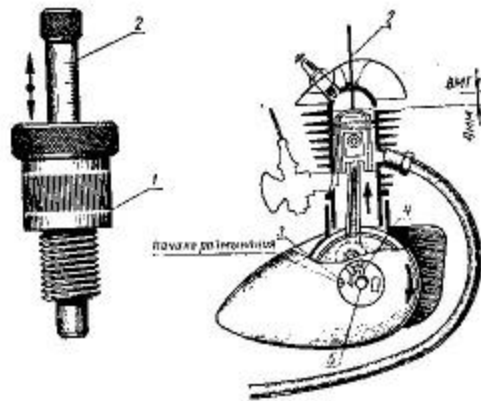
Установка и проверка опережения зажигания: 1 — корпус приспособления; 2 — шуп; 3 — свеча; 4 — молоточек; 5 — кулачок
